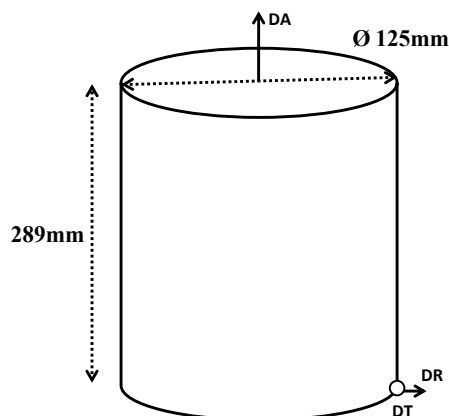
Schéma et dimensions du lopin avant forgeage
